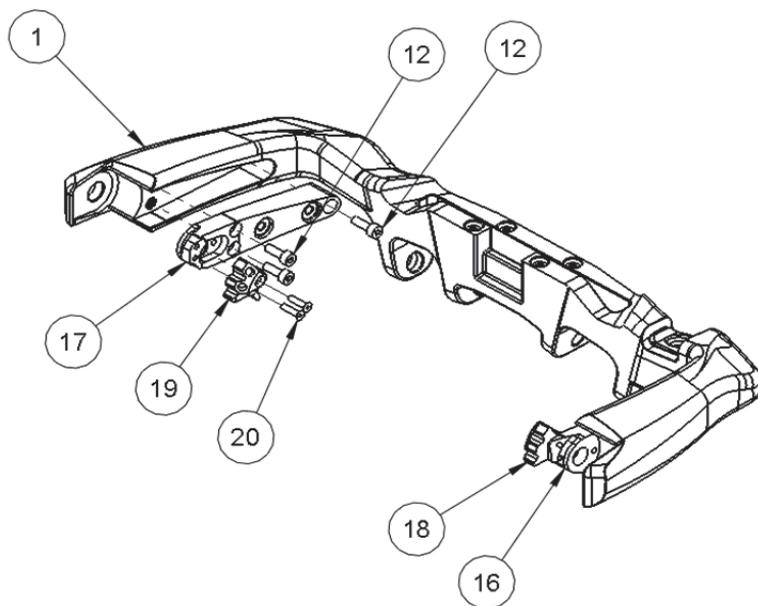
Vue éclatée — Assemblage arrière du scanner — Partie 2
